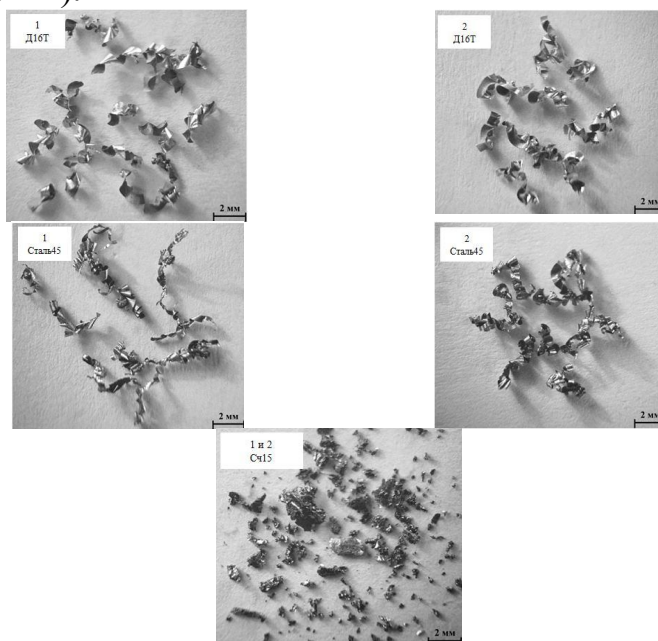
Формы стружки, образующейся при сверлении глубоких отверстий ружейными свёрлами $\varnothing 2,22$
